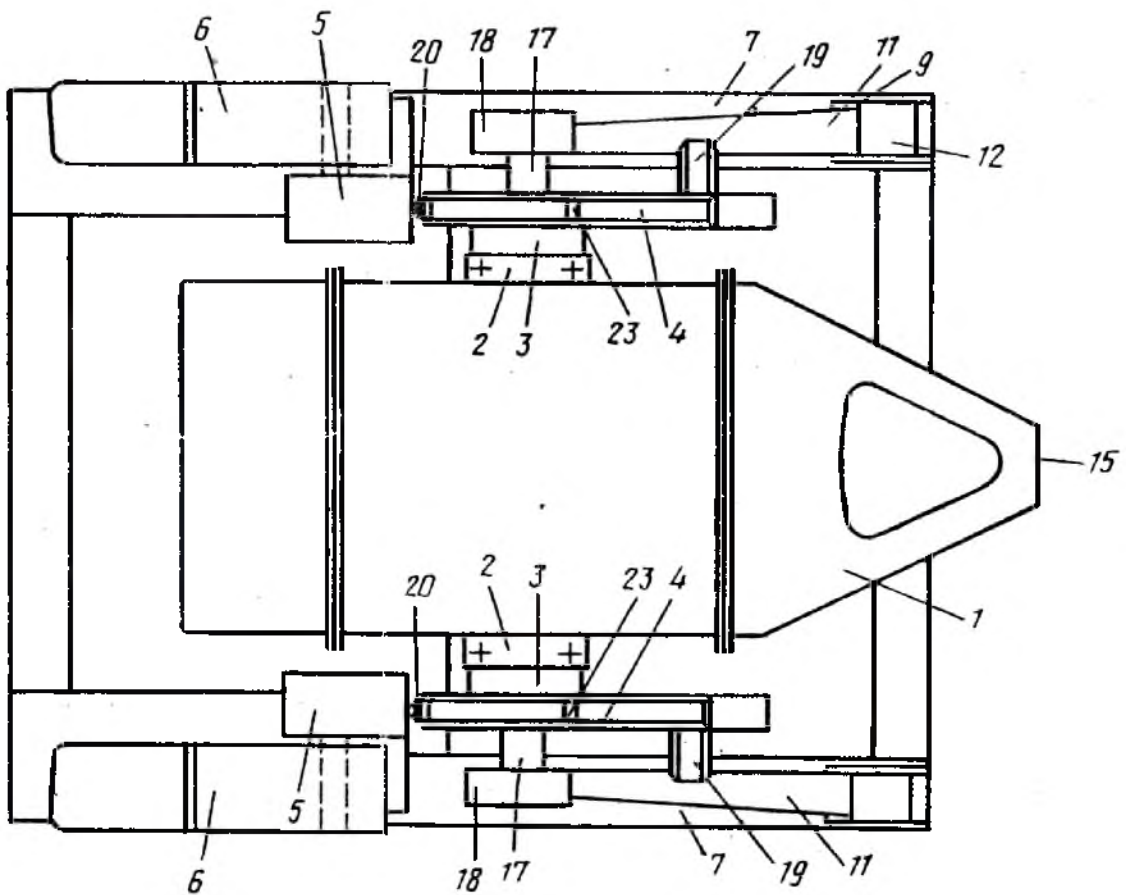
Пристрій для розливання металу (вид зверху)
